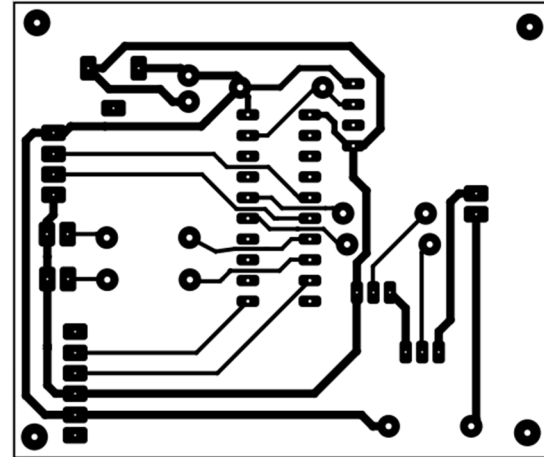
PCB1, Bottom view. Fuente: Autor.
